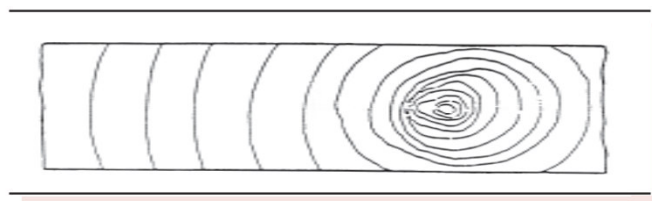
Sobre-espessura de cordão de soldadura
